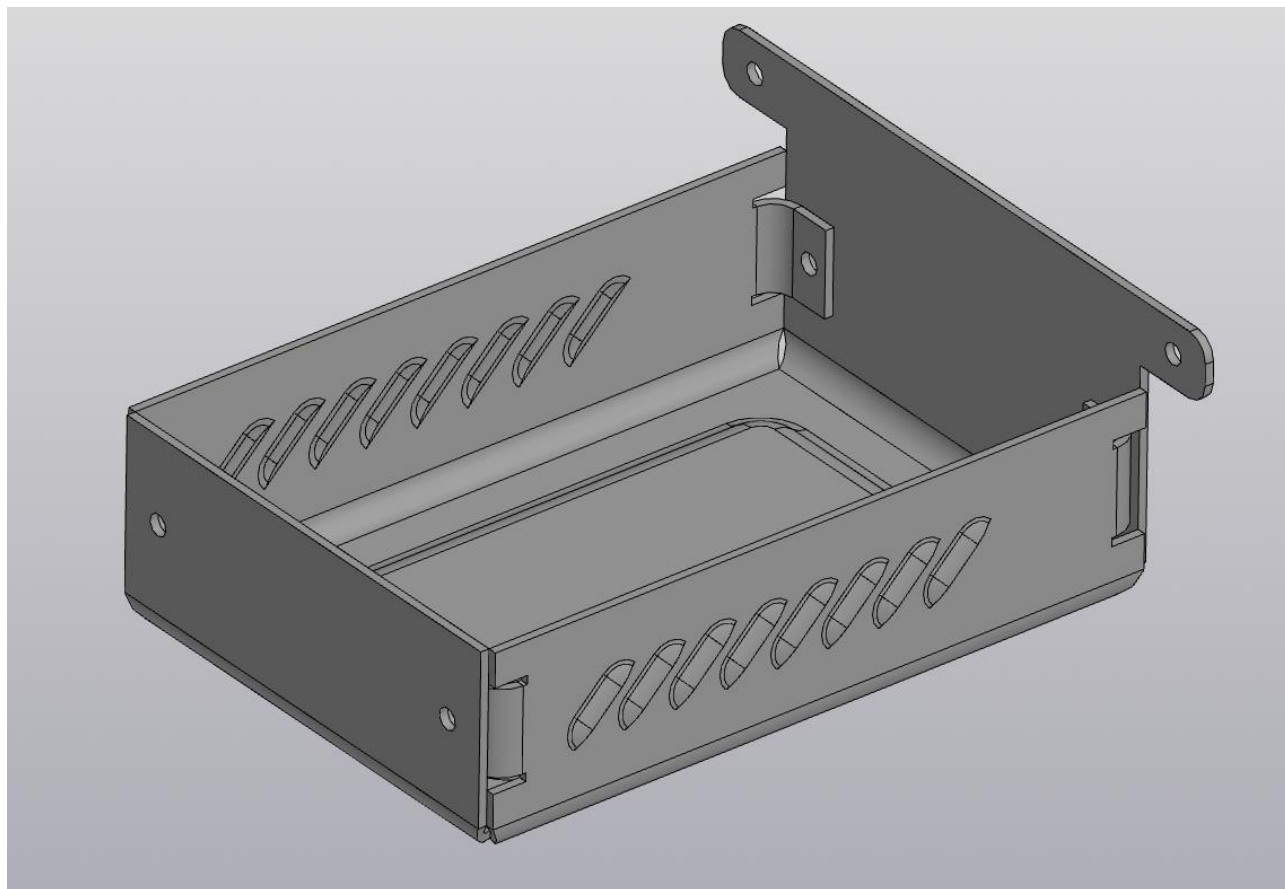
3D-модель детали «Корпус» (вариант 2)
